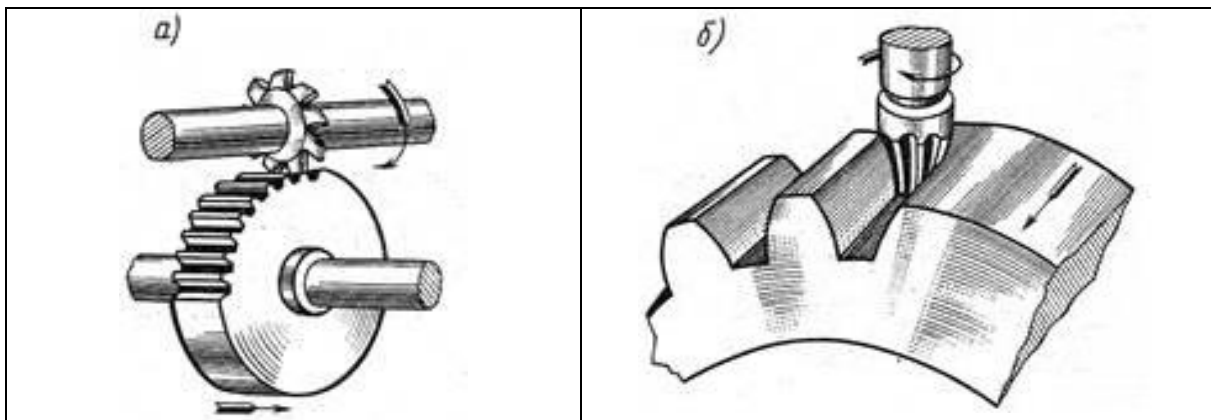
Нарізування зубчастих колес за методом копіювання:
